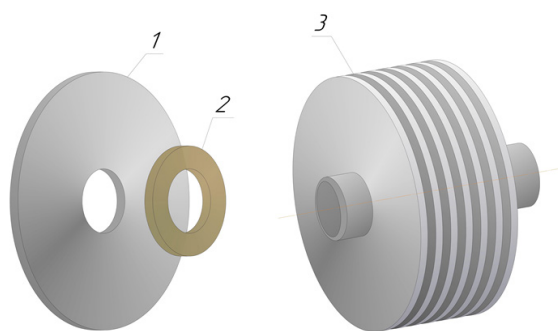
Сборка пакета заготовок дисковых ножей: 1 – заготовка дискового ножа; 2 – разделительная шайба; 3 – пакет заготовок дисковых ножей
